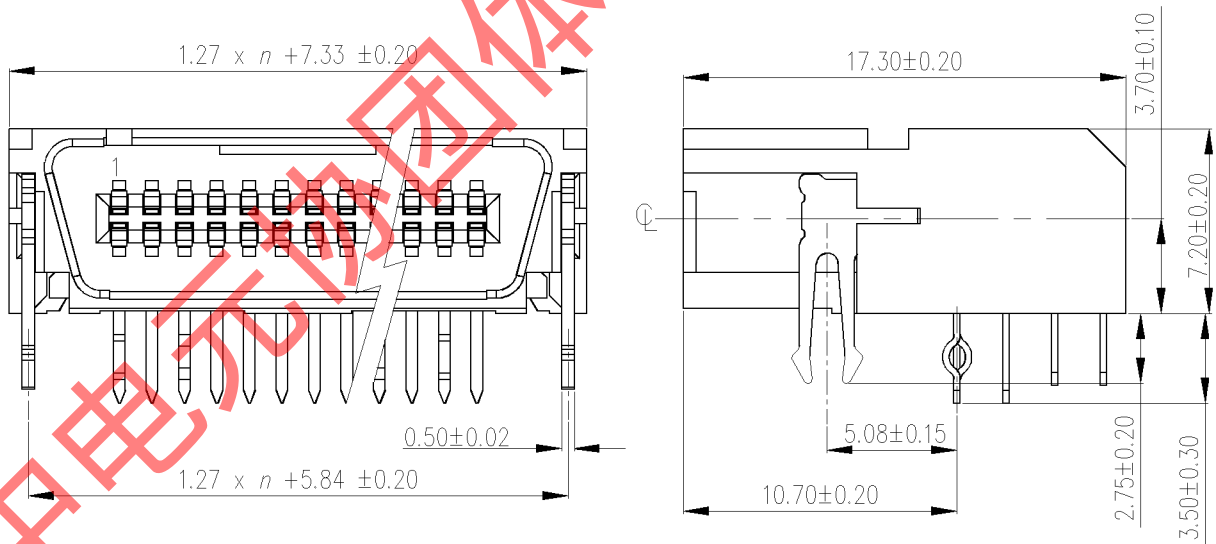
D 类型插头 90 度穿孔焊接式外形尺寸
